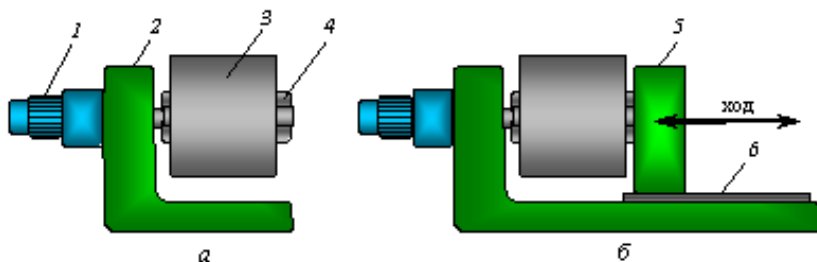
Барабанные моталки: а — консольная; б — 2-опорная; 1— мотор-редуктор; 2— корпус; 3 — бунт; 4— барабан; 5— отводная опора; 6— направляющие
